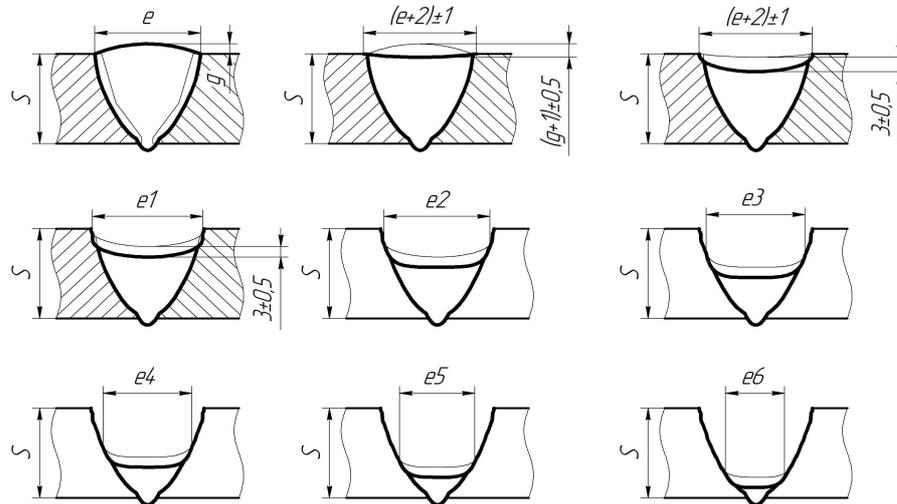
Геометрические параметры выборки кольцевого стыкового соединения воздушно-плазменной строжкой
